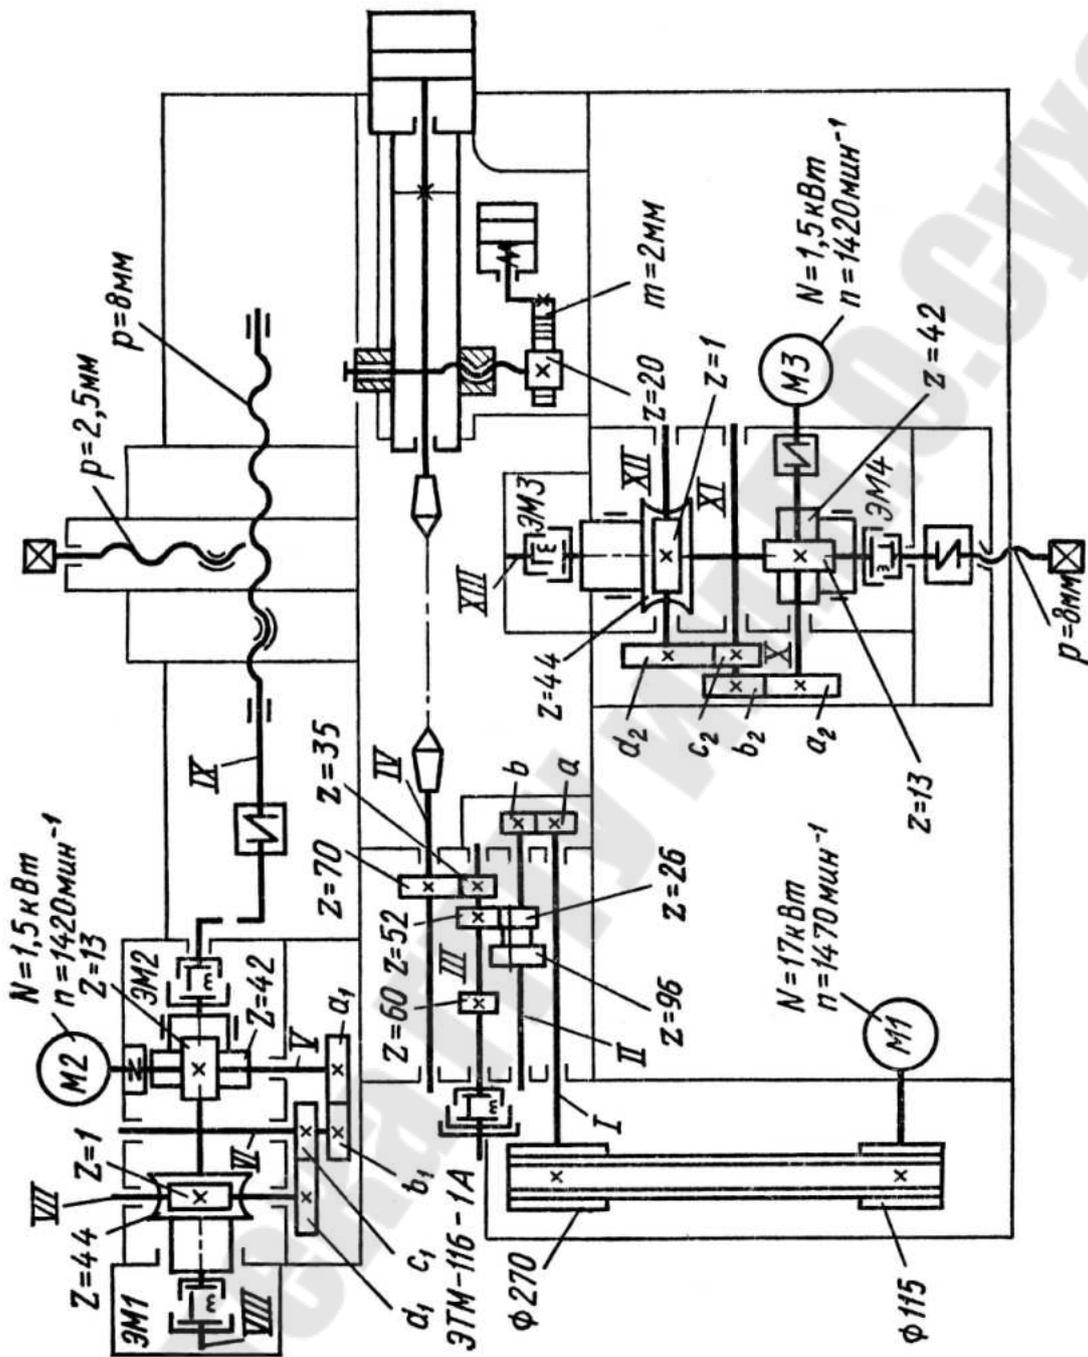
Кинематическая схема многорезцового токарного полуавтомата 1Н713
